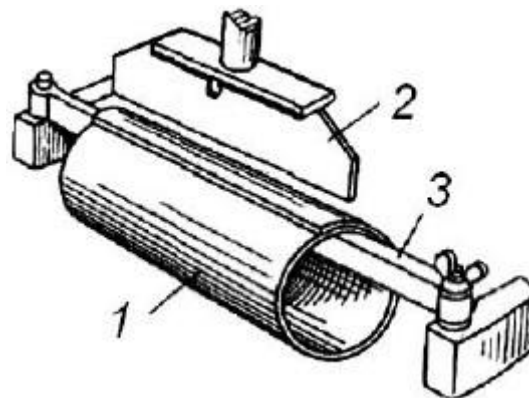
Схема сварки продольных швов труб из ПВХ: 1 – труба; 2 – высоковольтный электрод; 3 – шарнирный электрод материал
